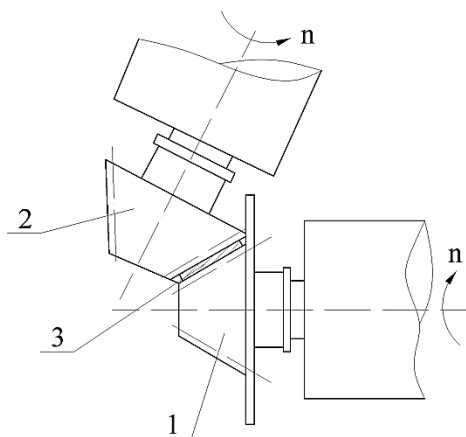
Схема утворення гофрованої поверхні кінчними колесами:
